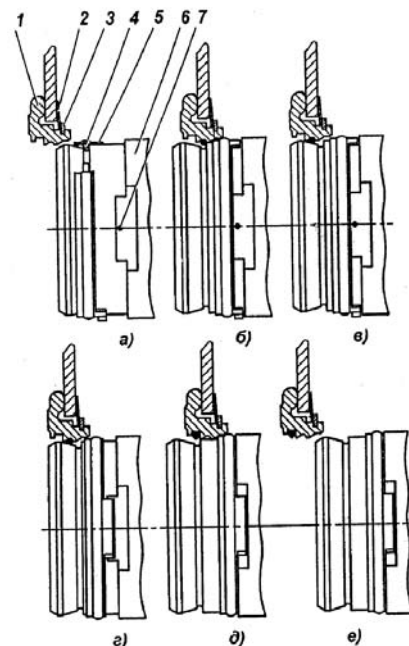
Основные положения запорного устройства: 1 — упорное кольцо; 2 — пружинная шайба; 3 — стопорное кольцо; 4 — пружинное кольцо; 5 — замковое кольцо; 6 — втулка подшипника; 7 — предохранительное кольцо
